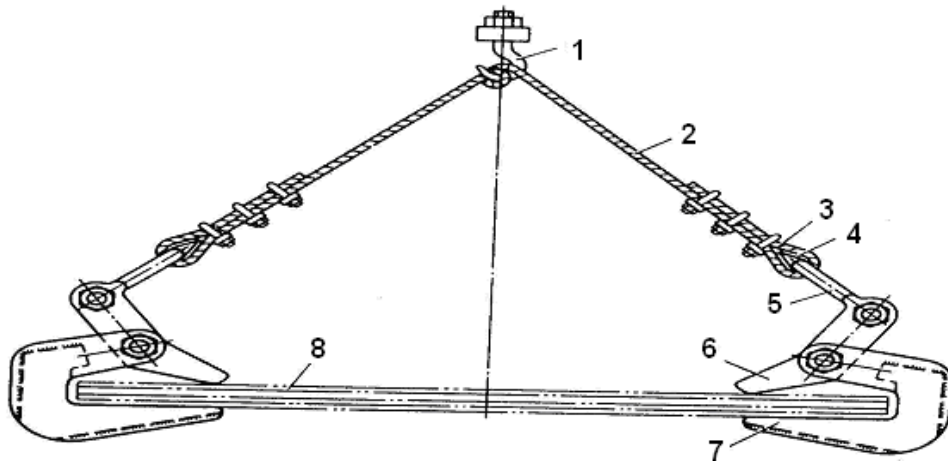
Захват для підіймання пакета листів металу:
